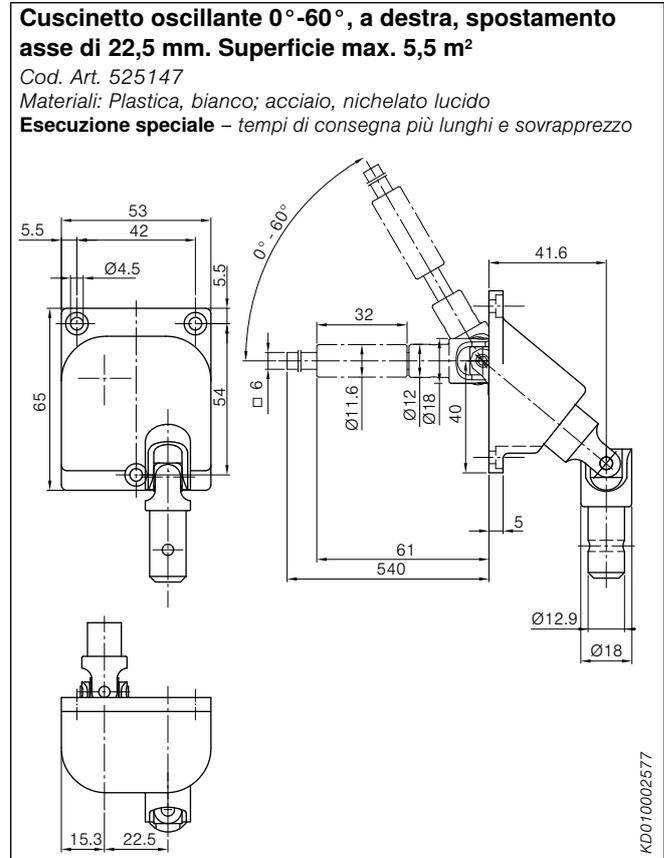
Cuscinetto oscillante 0°-60°, a destra, spostamento asse di 22,5 mm
